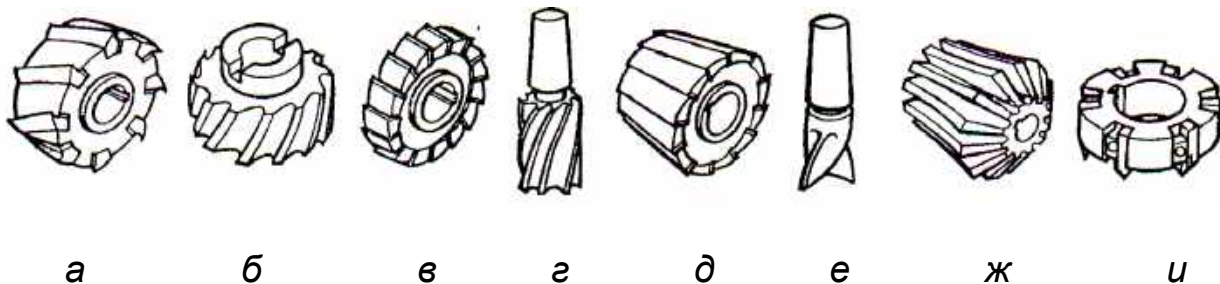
Фрези для оброблення поверхонь: а – циліндричні; б – торцеві; в – дискові; г – кінцеві; д – однокутові; е – шпонкові; ж – фасонні; и – торцеві насадні зі вставними різцями
